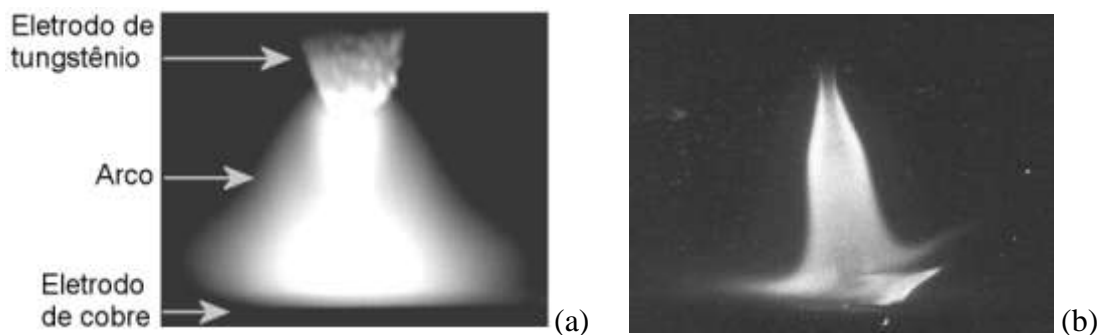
Aspecto típico do arco elétrico na soldagem (a) GTAW (Gas Tungsten Arc Welding) e (b) GMAW (Gas Metal Arc Welding).
